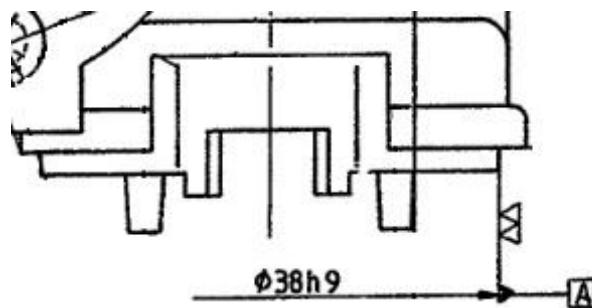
Toleranciamento da face exterior de diâmetro 38 mm
